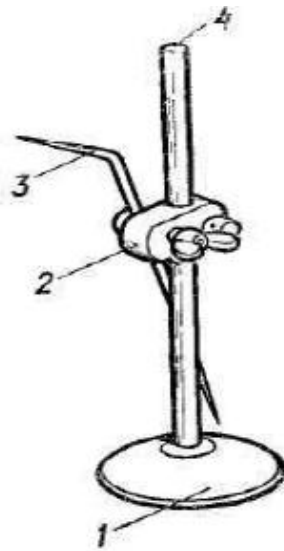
37. Рейсмус одногільчастий: 1 – основа; 2 – муфта; 3 – рисувалка; 4 – штатив
